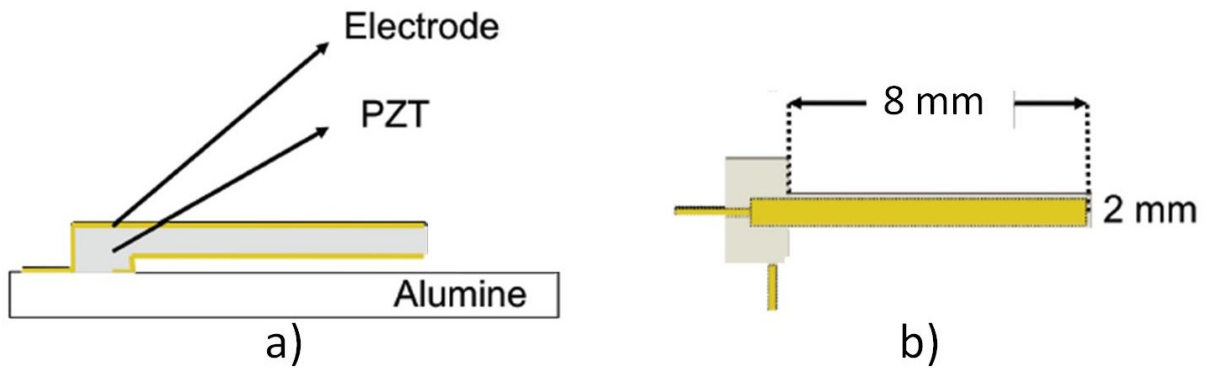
Géométrie et dimensions des micropoutres à réaliser - a) vue en coupe - b) vue de dessus
